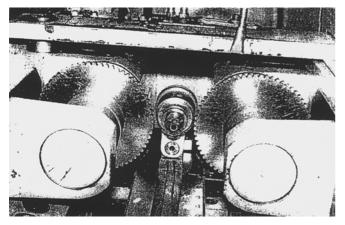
Приспособление для накатывания боковых поверхностей зуба венца коробки передач
